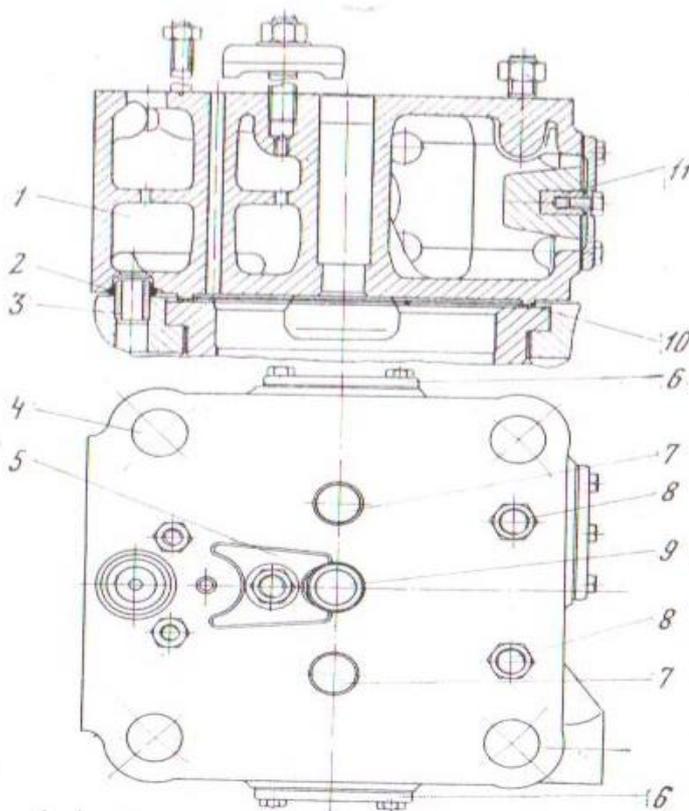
Головка цилиндра дизеля 4ДВ-224
